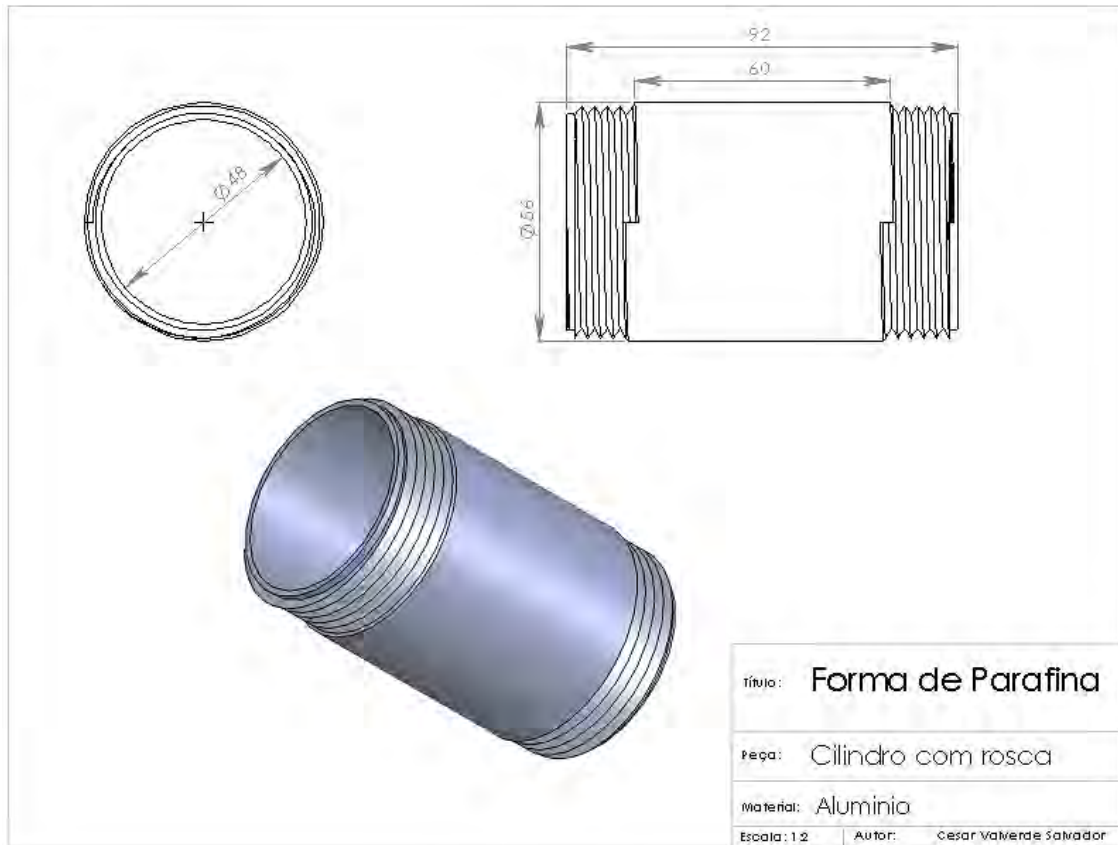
Desmontagem da forma cilíndrica, cotas do Cilindro de alumínio com rosca para posterior fabricação.
